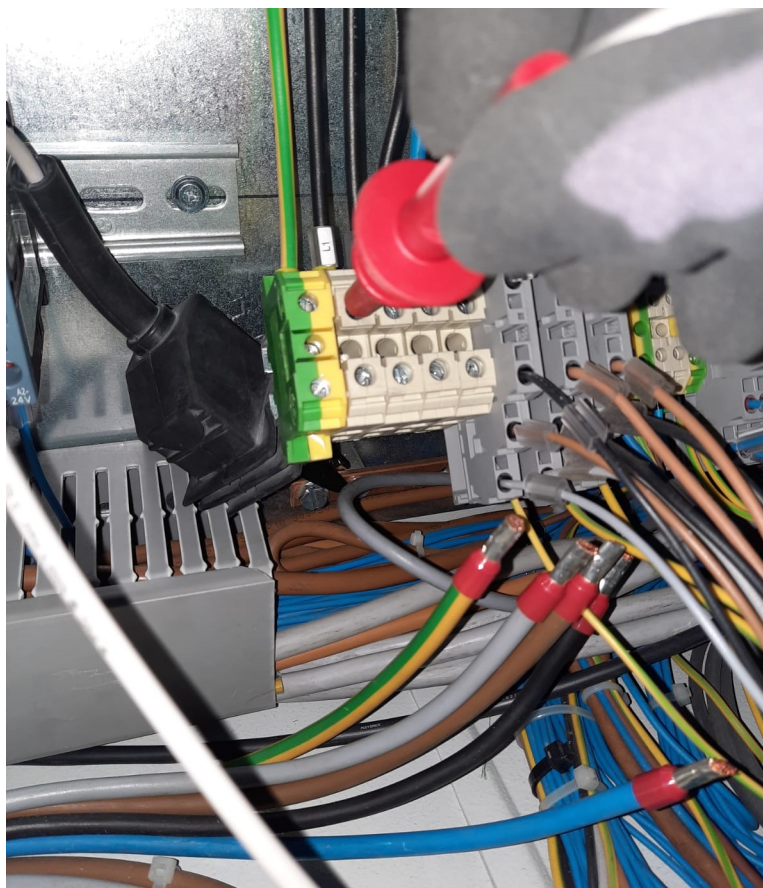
Collegamenti cavi e sezionamento dell'alimentazione per il test di tensione applicata
